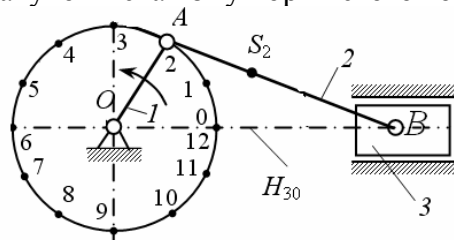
Схема механізму поршневого компресора аеродромної компресорної станції
